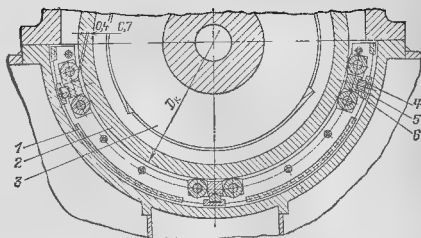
Опора качения колеса цилиндрической передачи ВПУ:
